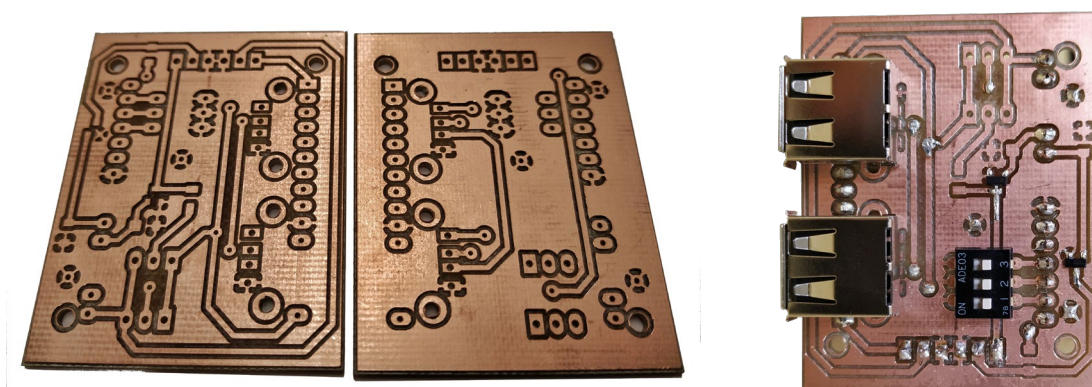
PCB realizada con la fresadora ProtoMat S62 (izquierda). Soldado de componentes a la PCB (derecha).
